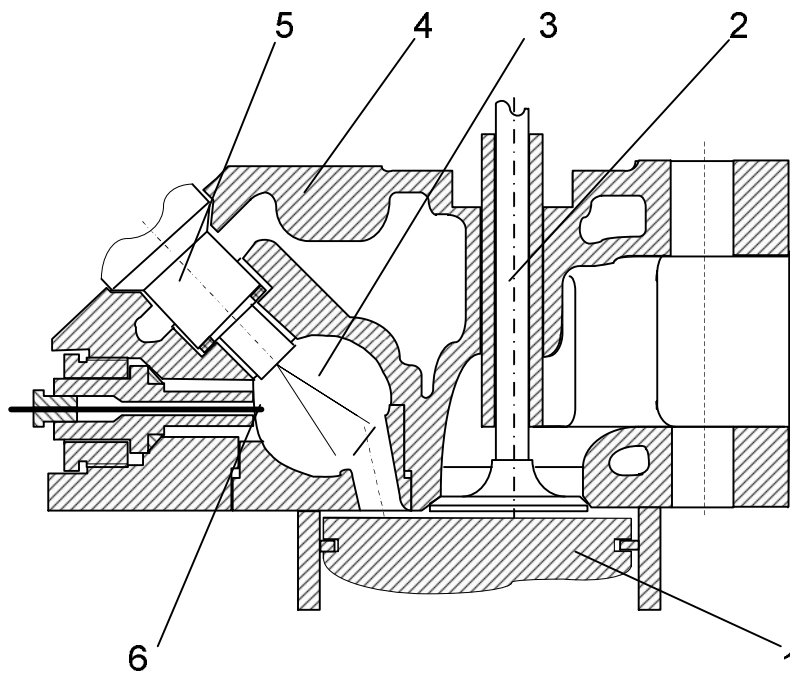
Схема камеры сгорания дизеля Ч 8,5/11: 1-поршень; 2-клапан; 3-вихревая камера сгорания; 4-головка; 5-форсунка; 6-термопара
